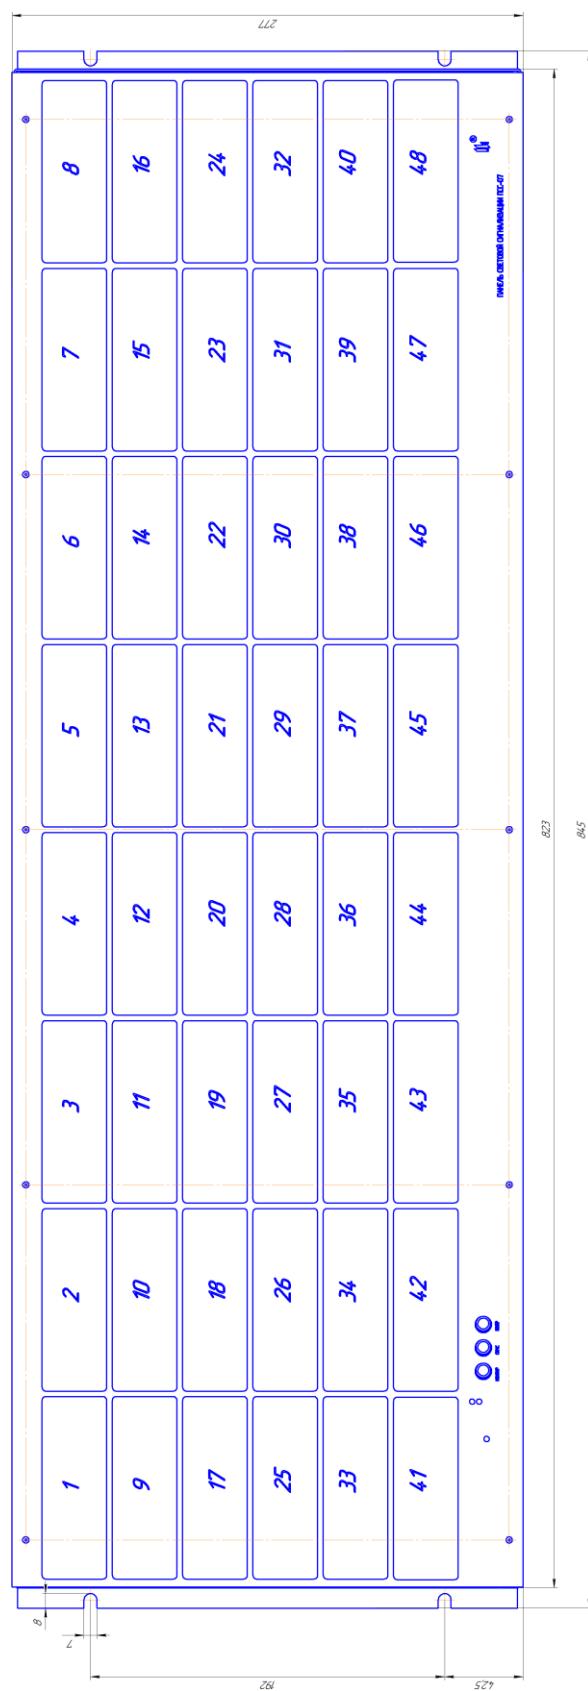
Габаритные размеры ПСС-07-09
